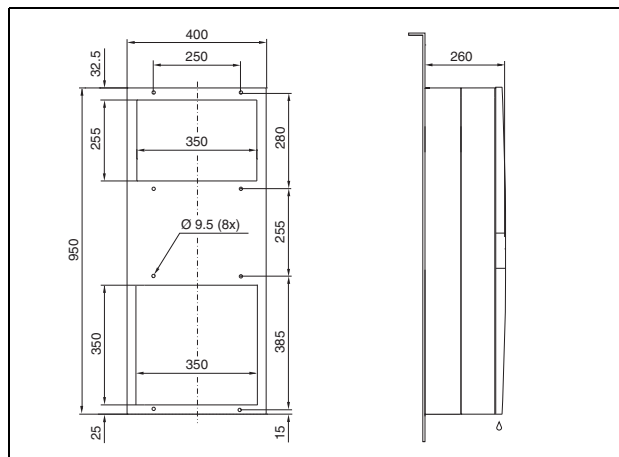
3304.xxx, 3305.xxx наружный монтаж
